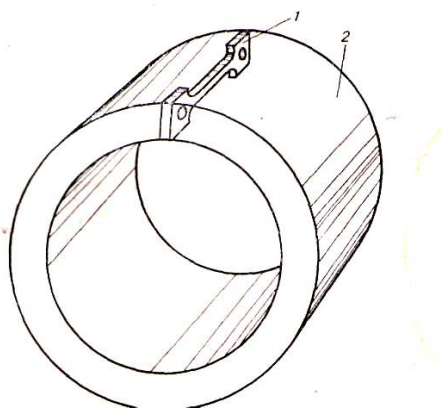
Схема вырезки образцов из наплавленного металла: 1 – общий вид образца; 2 – слой наплавленного металла
